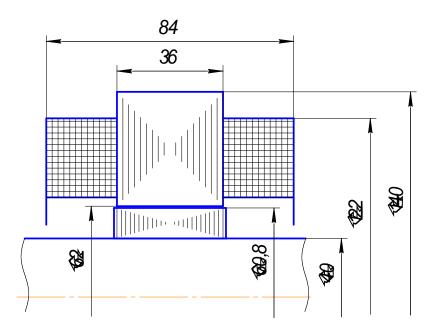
Габаритные размеры радиального электромагнитного подшипника
